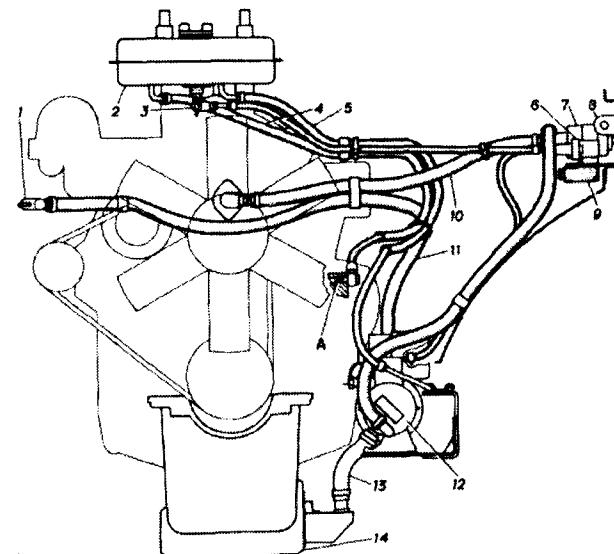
Установка пускового подогревателя и его оборудования:
